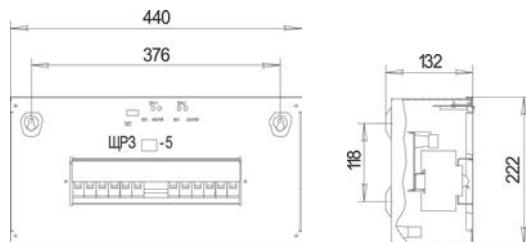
Габаритный чертеж ЩРЗ 24-5(С),
